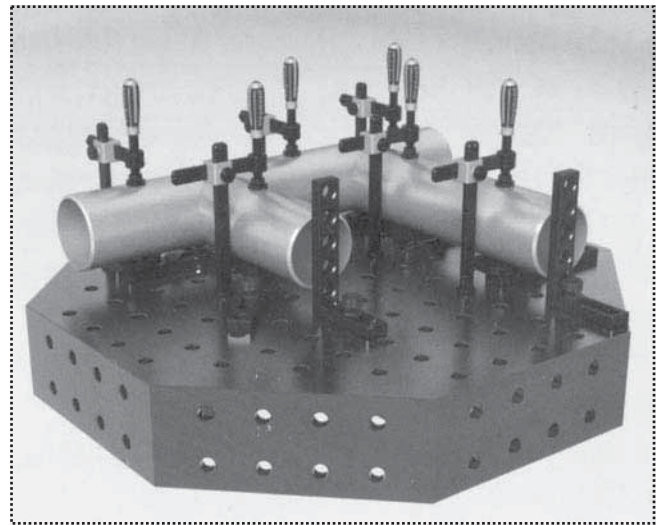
Восьмиугольный стол для роботизированной сварки
